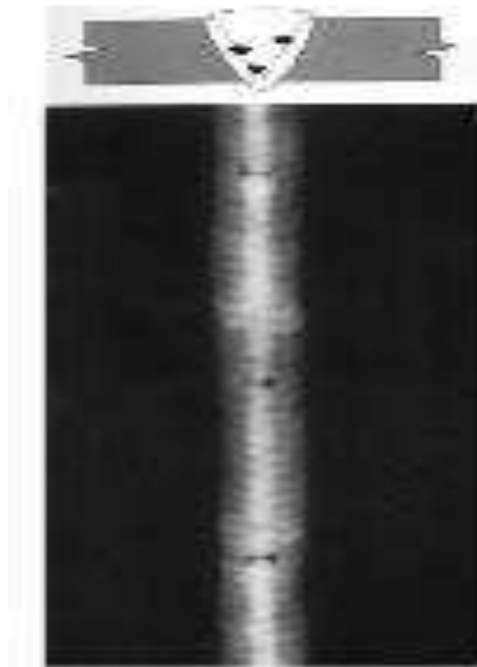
Porosidad esférica aislada en soldadura.
